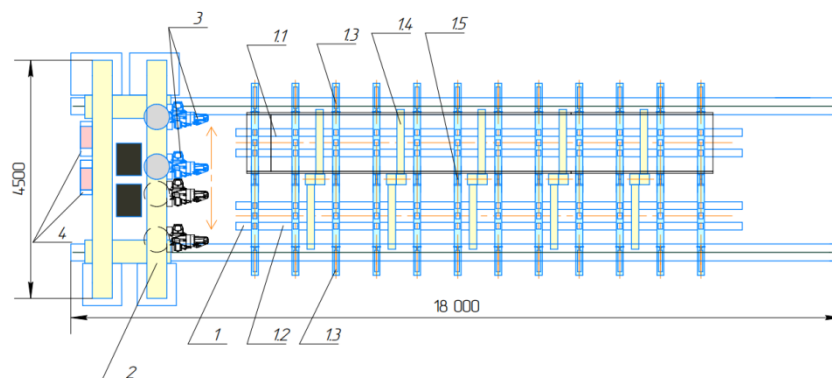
Установка для складання та автоматичного зварювання двотаврових балок: 1. Складальний стенд; 1.1. Перша позиція стенду; 1.2. Друга позиція стенду; 1.3. Гідравлічні притиски; 1.4. Кантувач; 1.5. Упори; 2. Портал зі зварювальним обладнанням; 3. Комплект зварювального обладнання для SAW-зварювання (під флюсом); 4. Комплект зварювального обладнання для MIG-MAG зварювання
